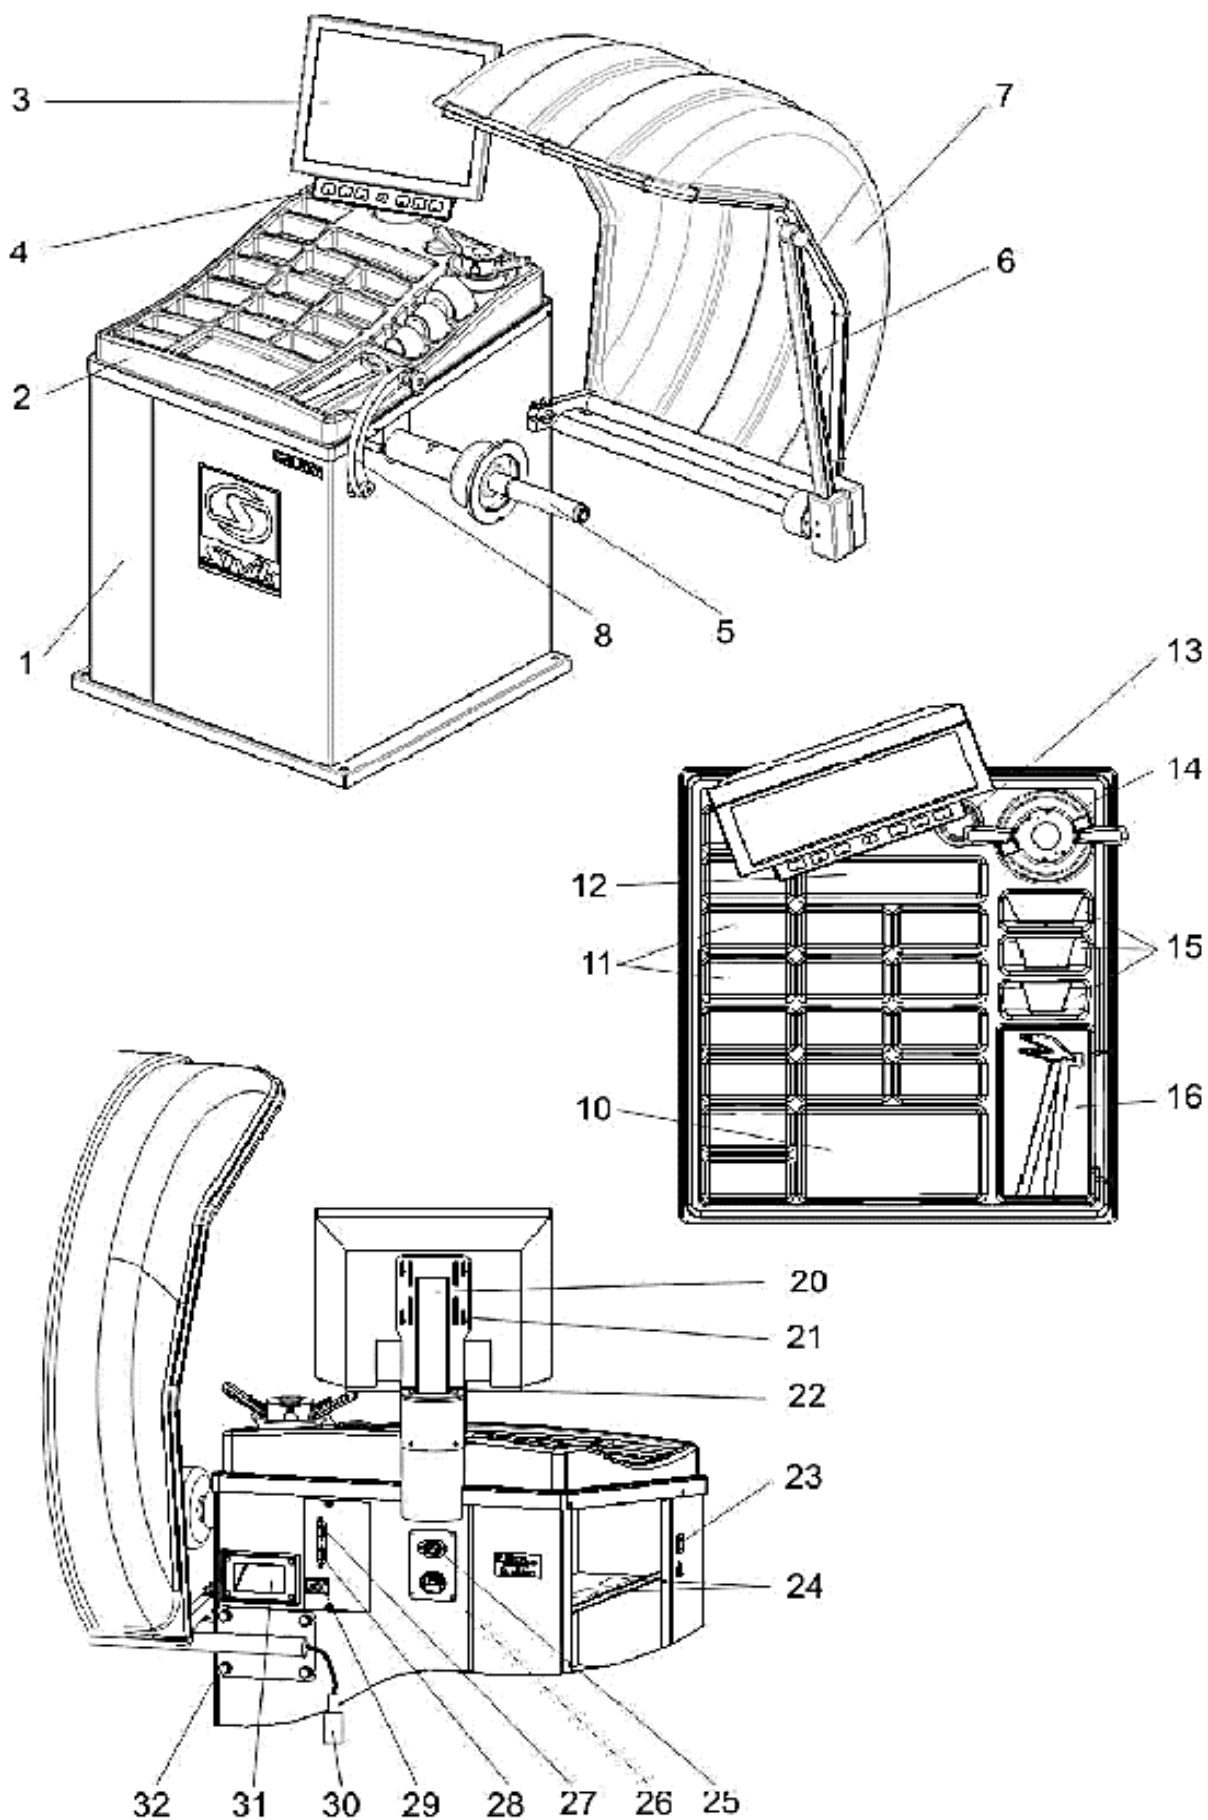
Конструкция станка балансировочного модель SBMP-60/3D
